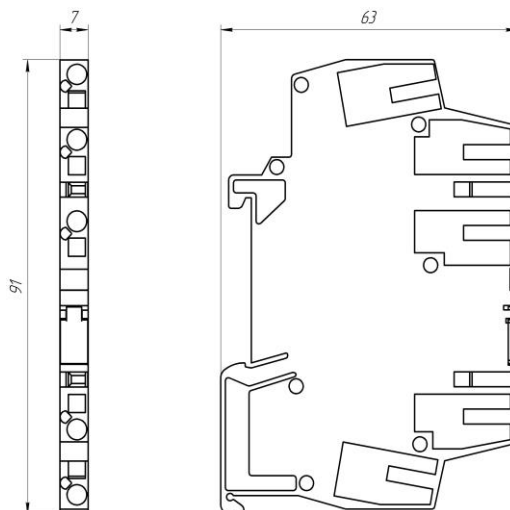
Внешний вид и габаритные размеры модуля DO-620-R
